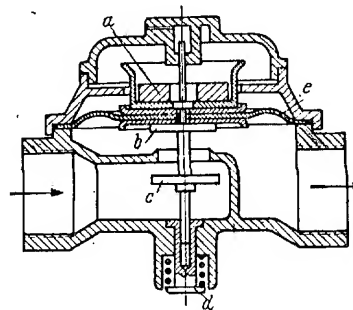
Unmittelbarer Gasdruckregler mit Gewichtsbelastung (Gleichwertregler).
